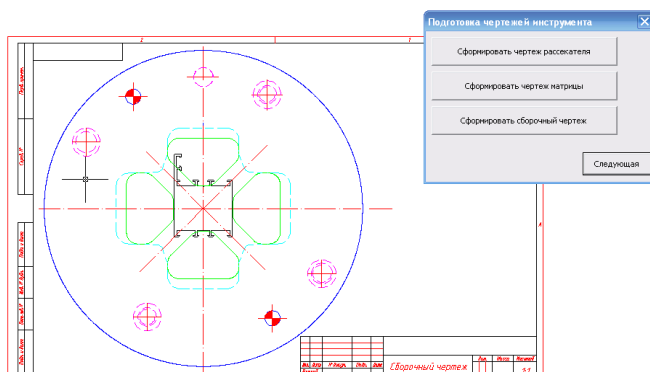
Пример подготовки чертежа инструмента для полого профиля КП 4545
